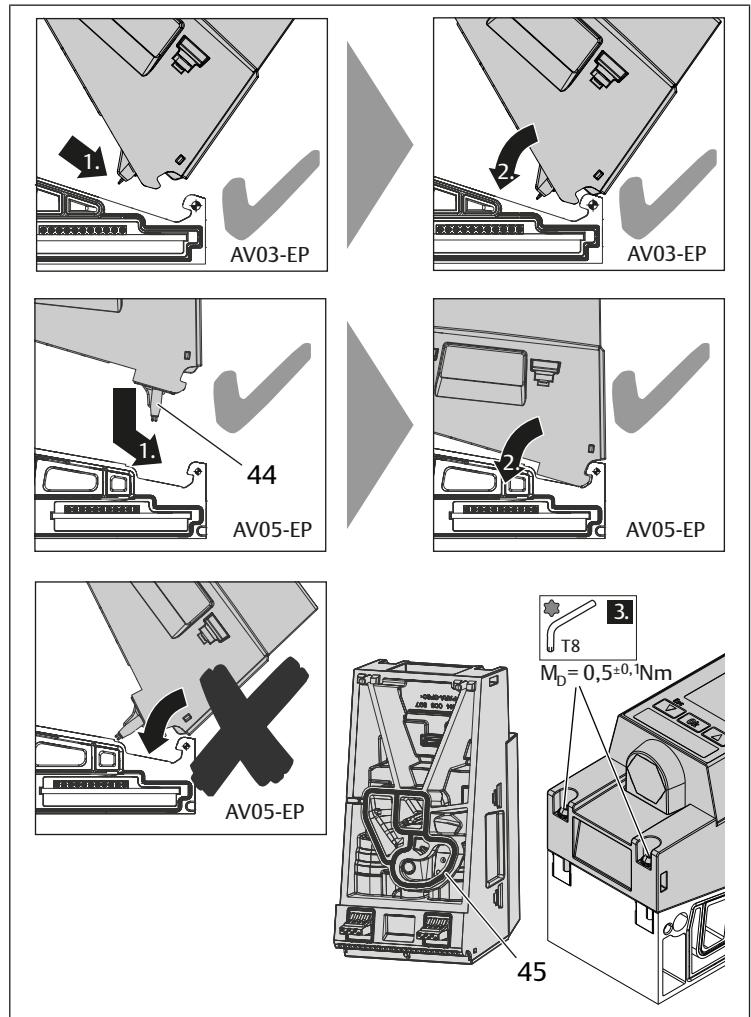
AV-EP-Druckregelventil auf die Grundplatte montieren
